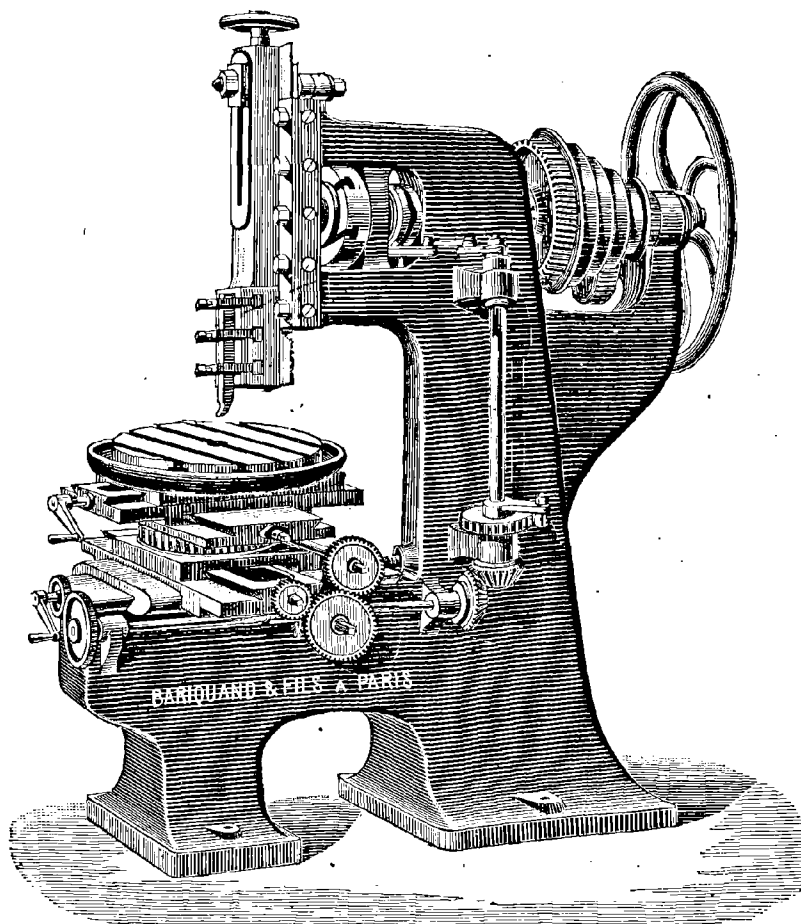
Machine à mortaiser de MM. Bariquand et Marre.
